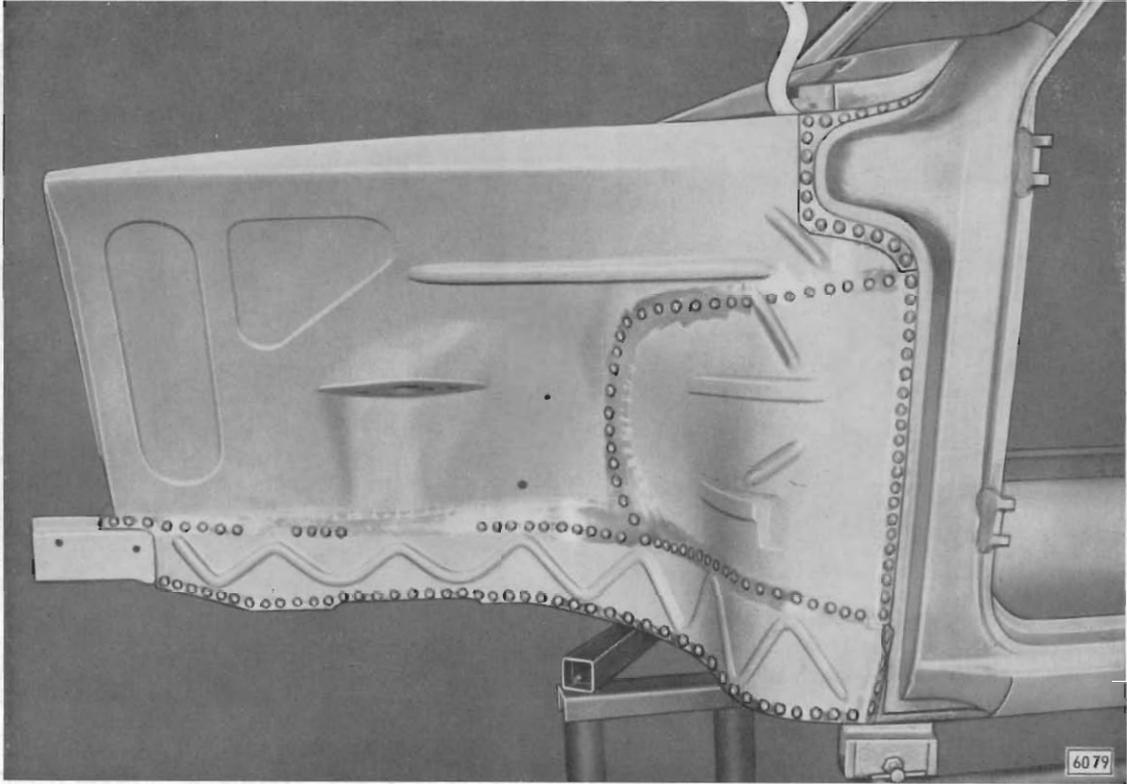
Radeinbau an Längsträger, Stirnwand, Türscharniersäule und senkrechten Flansch der Einstiegverkleidung punktgeschweißt
